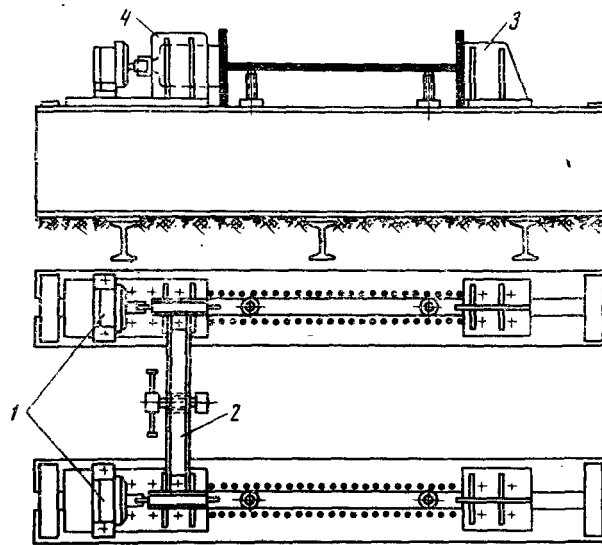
Сборочный кондуктор с пневматическими прижимами:
